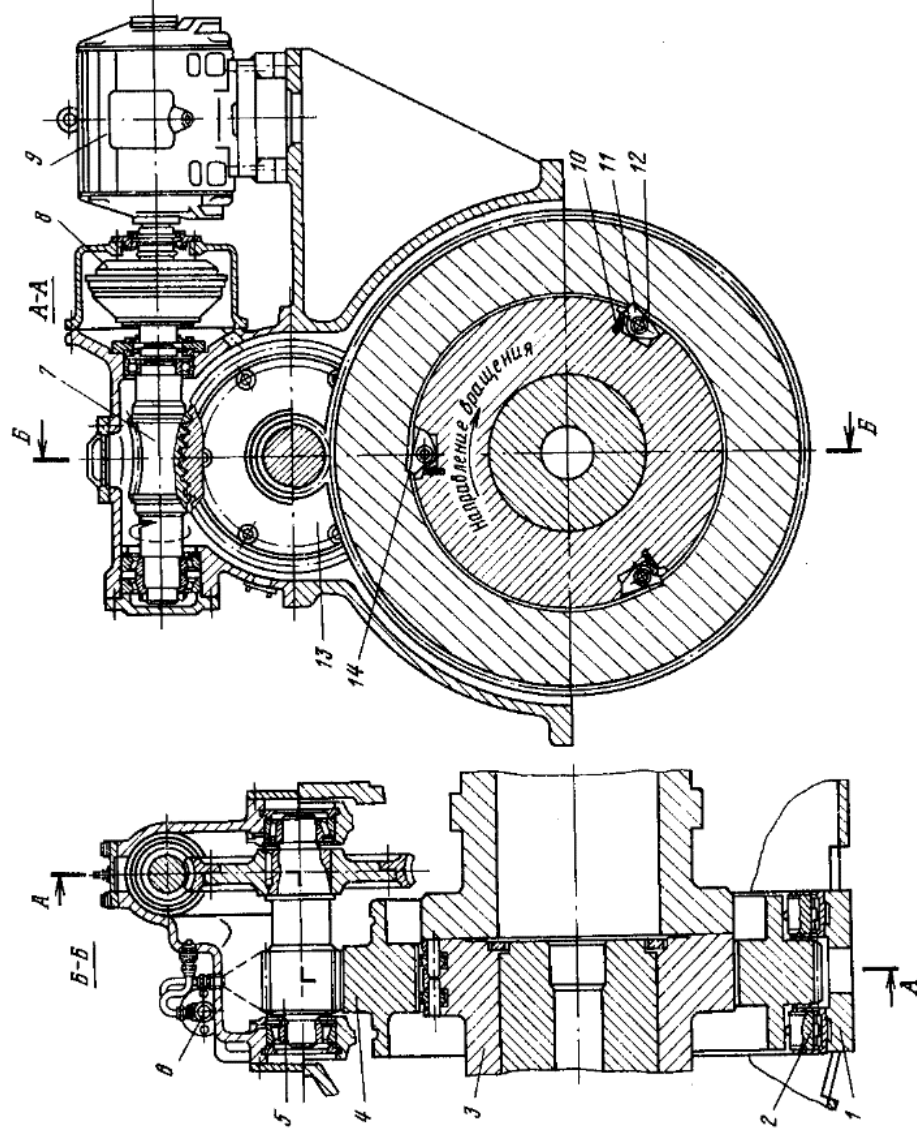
Валоповоротное устройство ХТЗ: 1 – корпус ЦНД; 2 – опора качения; 3 – ротор турбины; 4 – зубчатое колесо; 5 – вал-шестерня; 6 – коллектор смазки; 7 – червяк; 8 – гидромуфта; 9 – электродвигатель; 10 – пружина кулака; 11 – кулак; 12 – ось кулака; 13 – червячное колесо; 14 – поверхность контакта кулака и ротора турбины
